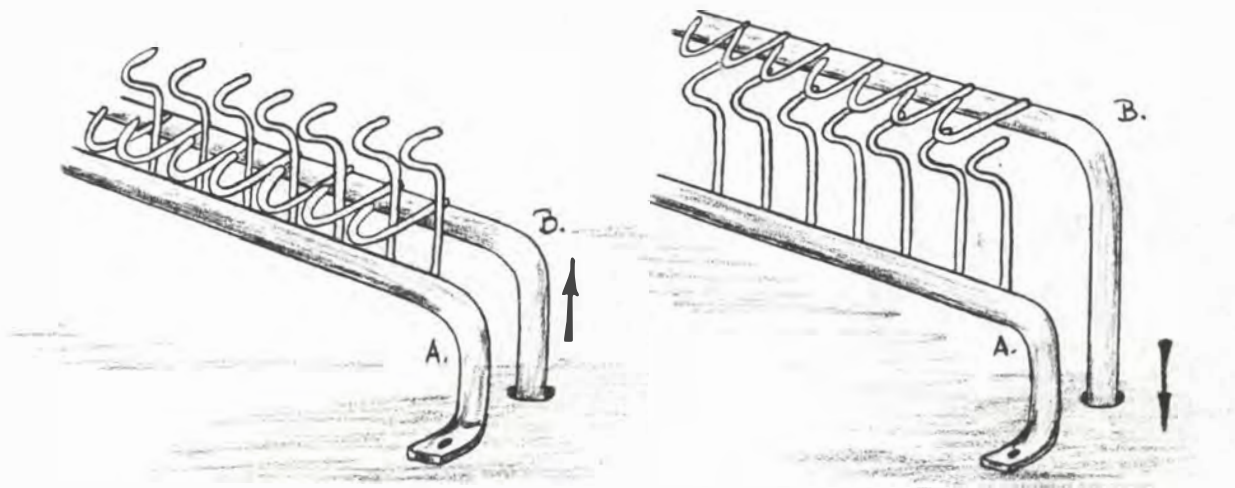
Detalle de los ganchos de las varillas A y B.
